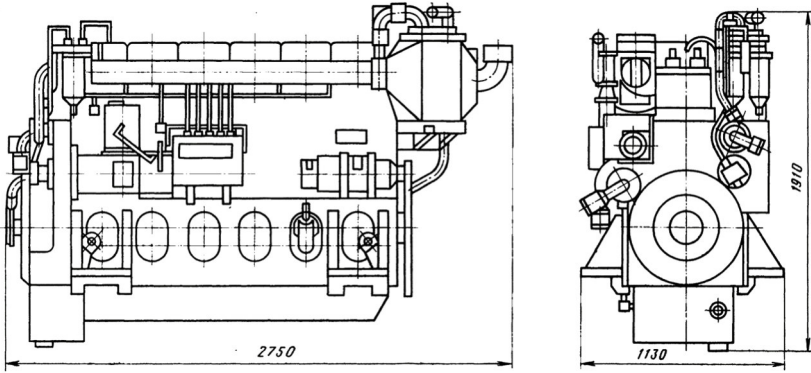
Габаритні креслення дизеля 6ЧН 21/21
